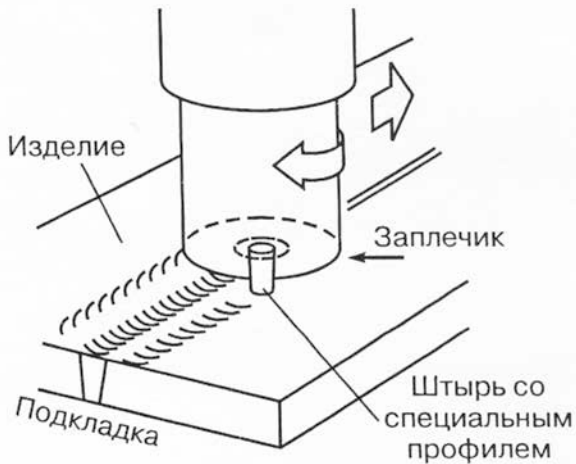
Схема процесса сварки трением с перемешиванием
